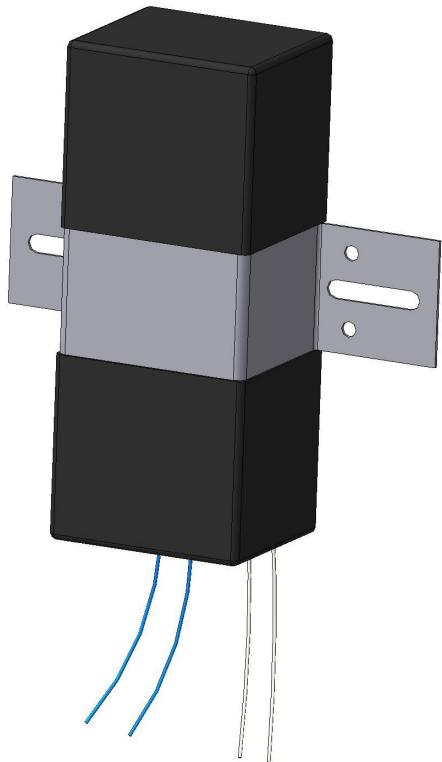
Внешний вид ДК-Ф со скобой крепления к стене
